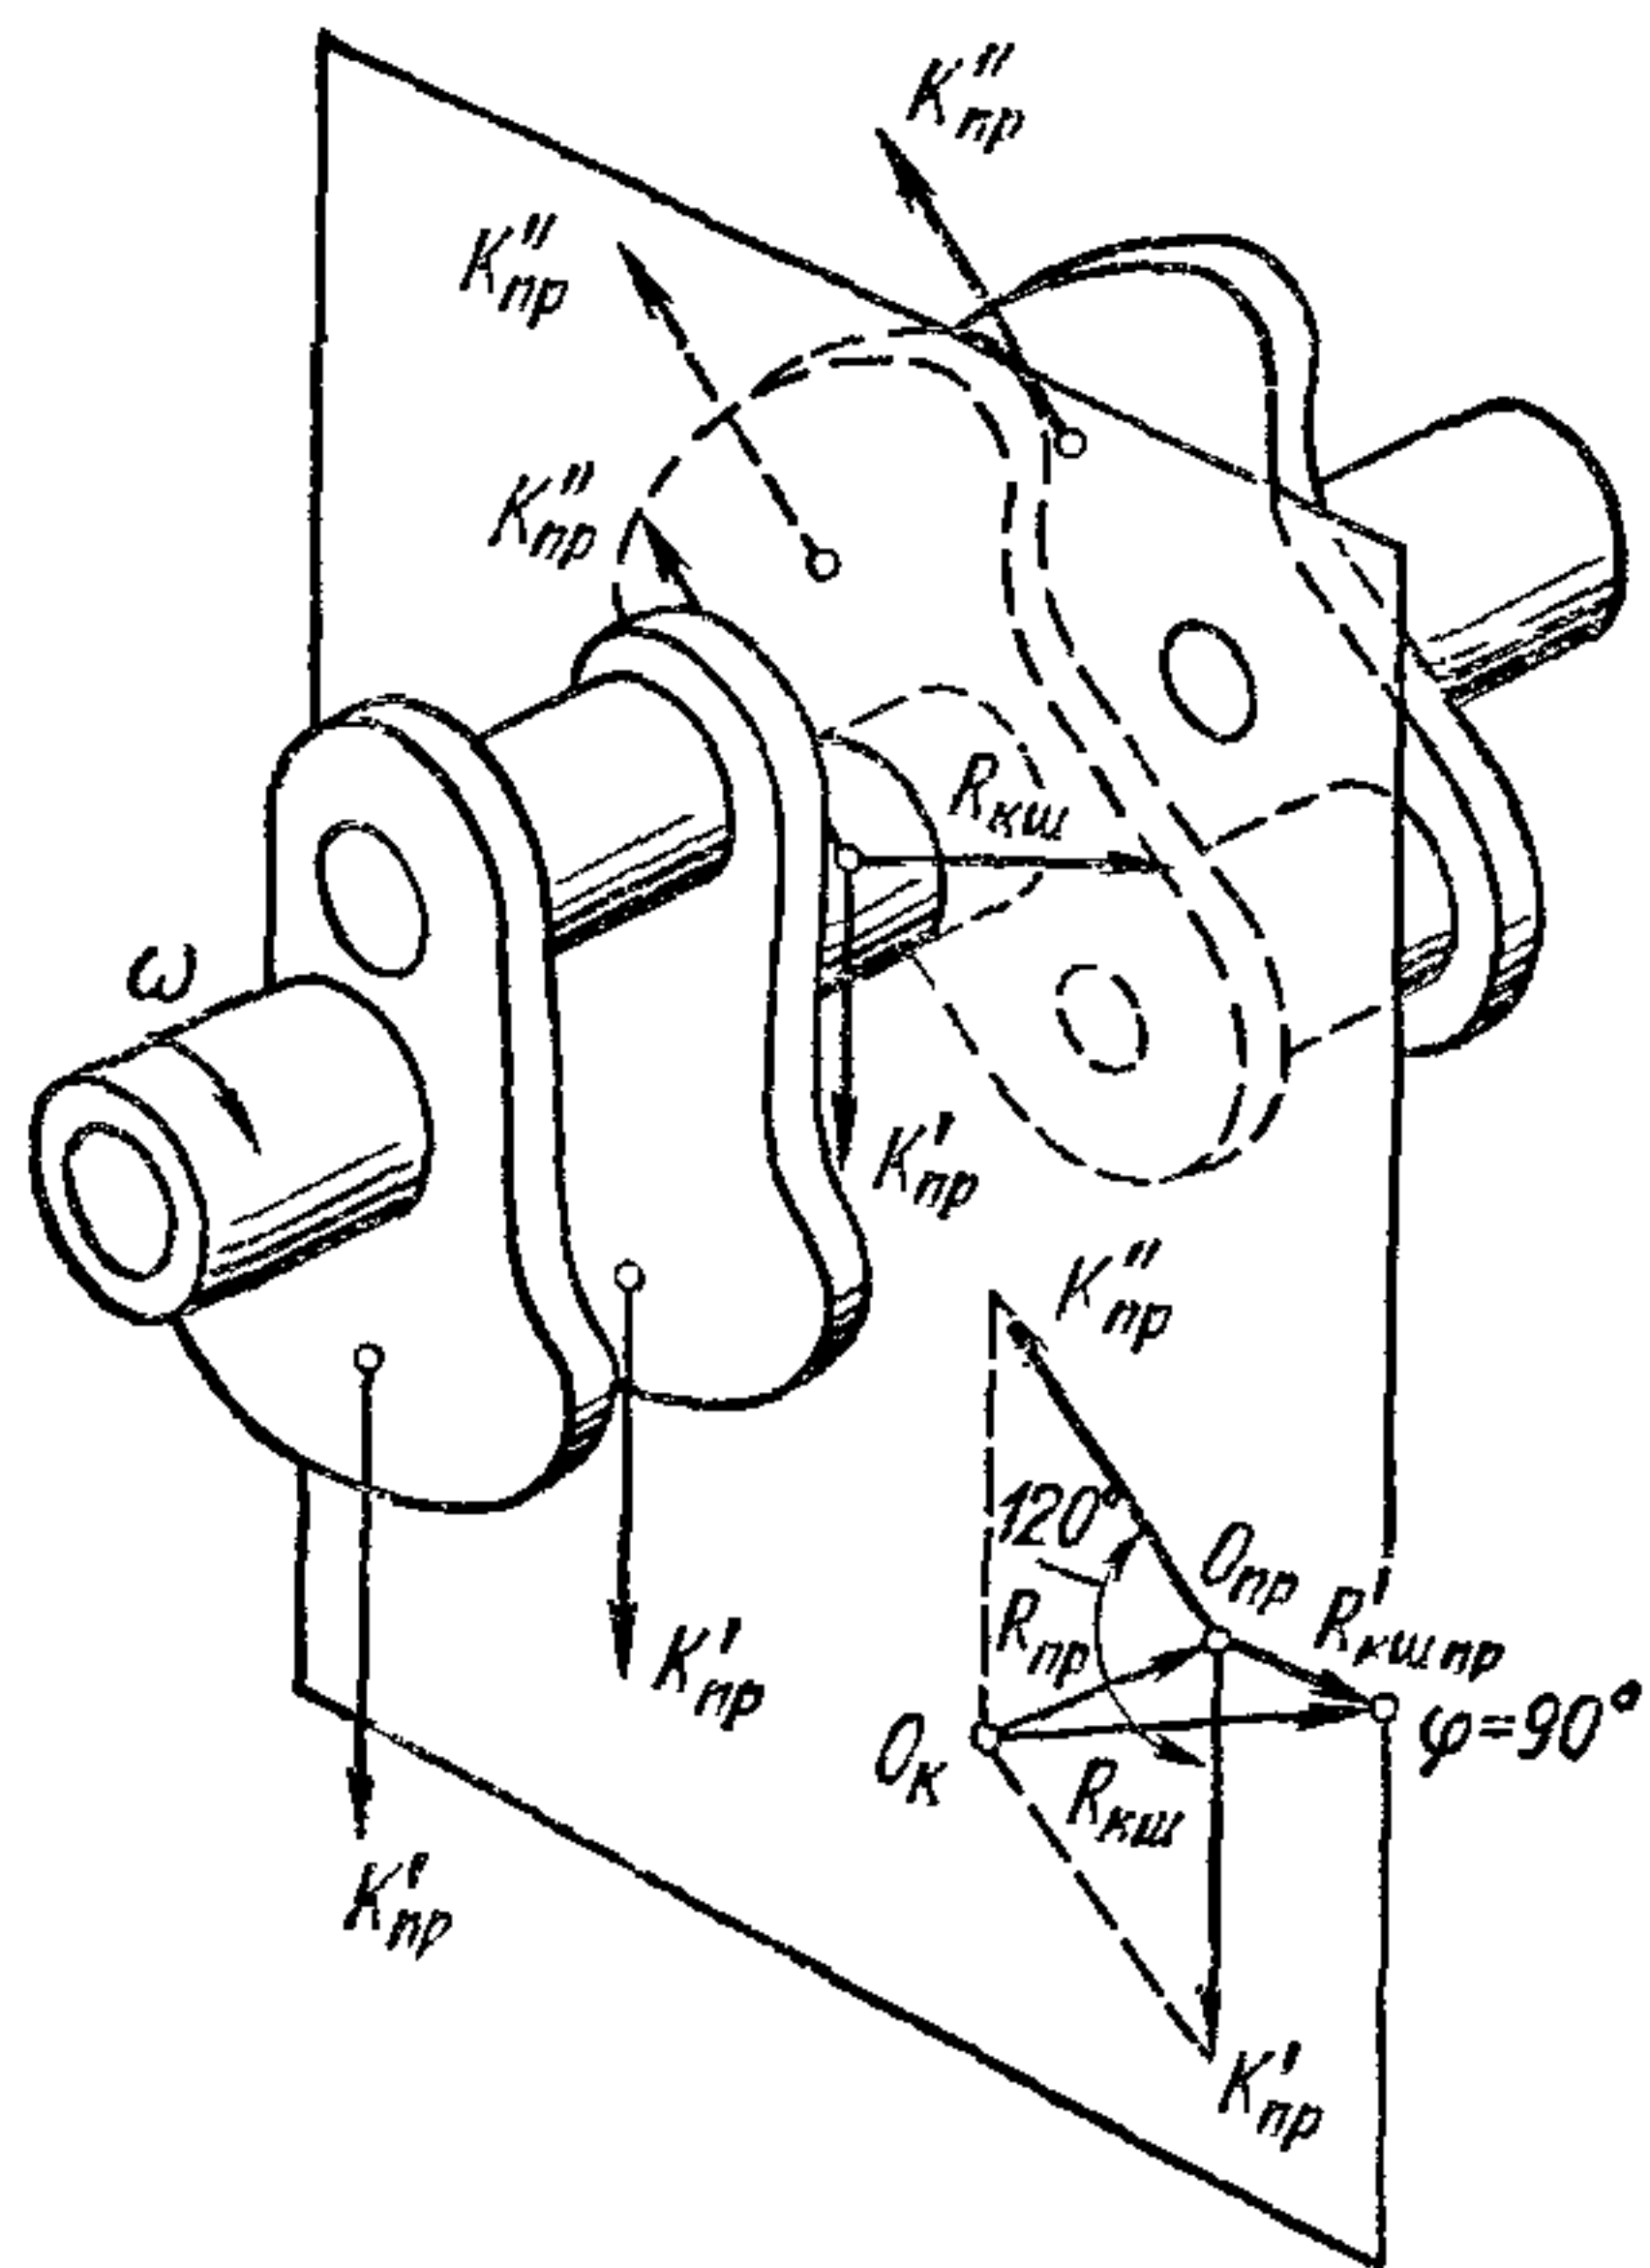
Разгрузка коренной шейки вала путем установки противовесов
